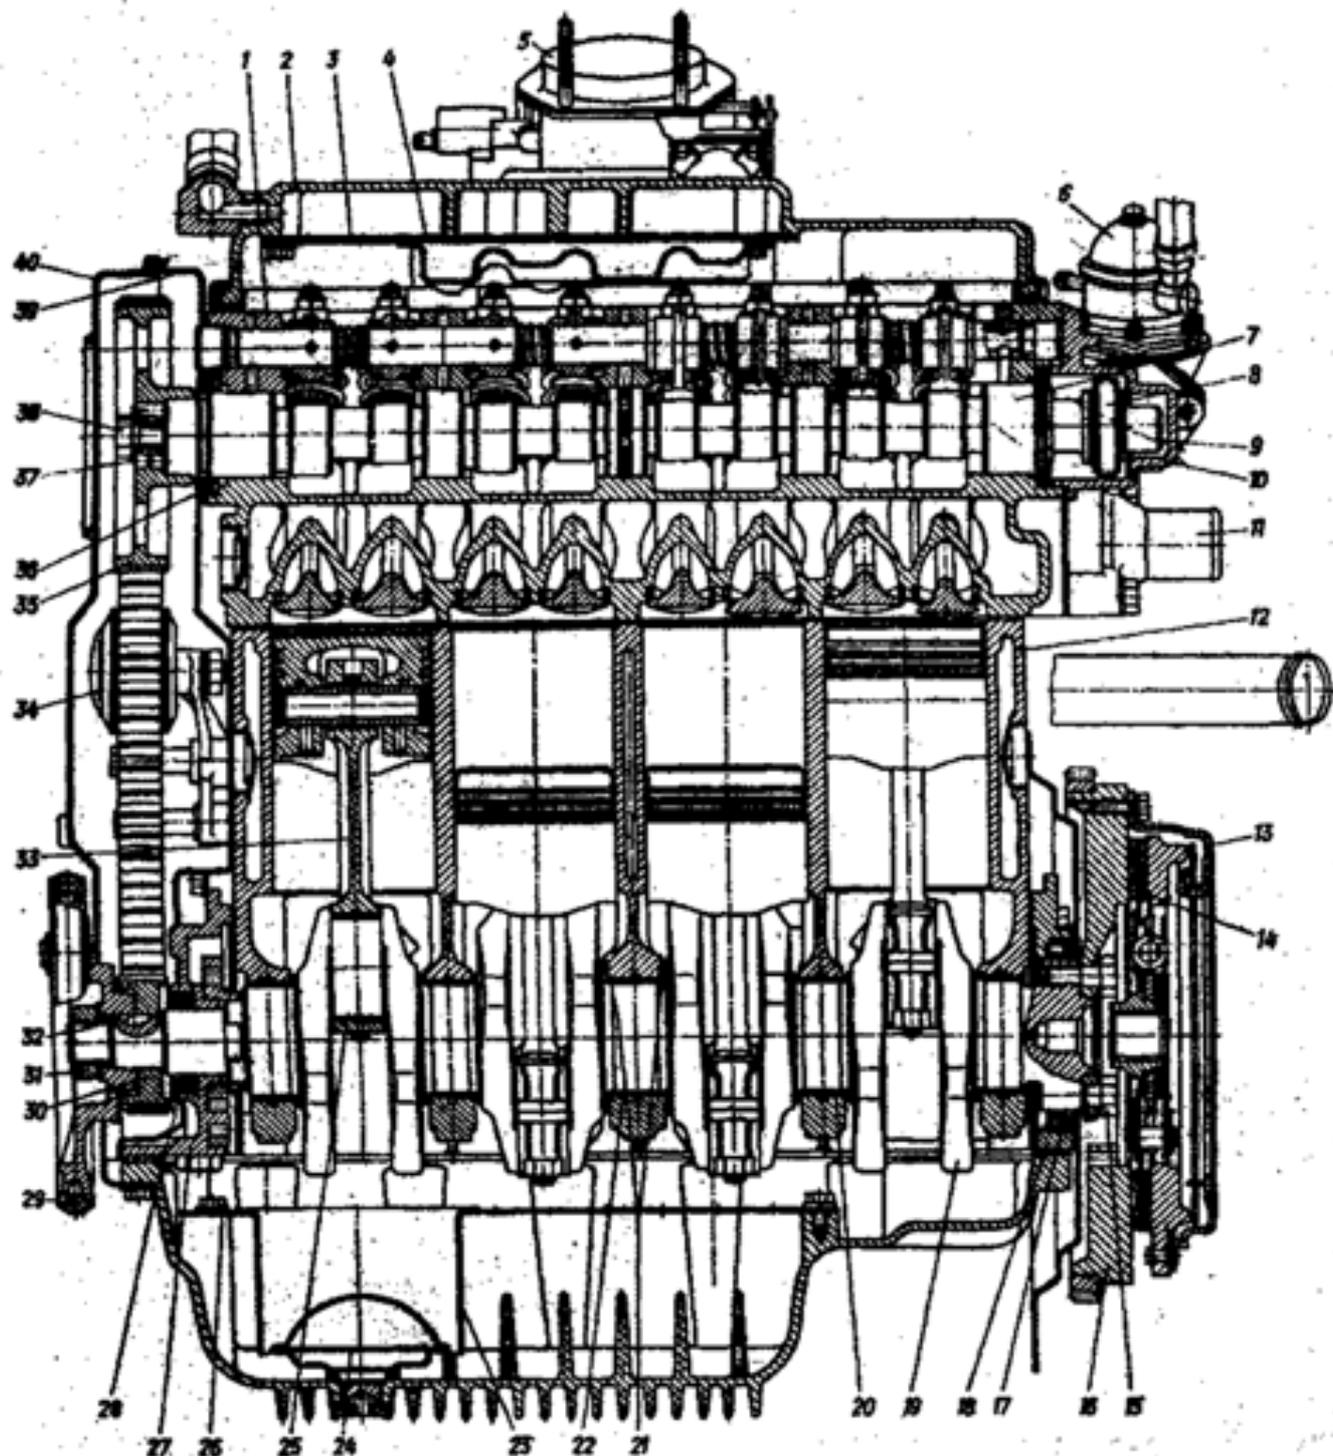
Продольный разрез двигателя: 1-головка цилиндров; 2-крышка головки цилиндров; 3, 4-прокладка и крышка маслоотделителя; 5-фланец карбюратора для крепления воздушного фильтра; 6-бензиновый насос; 7-вал распределительный; 8-ведущая шестерня привода датчика распределителя; 9-кулачок привода бензинового насоса; 10-корпус привода датчика-распределителя и бензинового насоса; 11-отводящий патрубок; 12-блок цилиндров; 13-нажимной диск сцепления; 14-диск сцепления ведомый; 15,38-болты; 16-маховик; 17,28,36-манжеты; 18-держатель манжеты; 19-коленчатый вал; 20-вкладыши коренных подшипников коленчатого вала; 21-упорные полукольца коренного подшипника коленчатого вала; 22-вкладыш среднего коренного подшипника коленчатого вала; 23-приемник масляного насоса; 24-маслосливная пробка; 25-вкладыш нижней головки шатуна; 26-масляный картер; 27-масляный насос; 29-шкив привода генератора; 30-ведущий шкив коленчатого вала; 31-гайка; 32-шпонка; 33-шатун с поршнем, поршневыми кольцами и пальцем; 34-натяжной ролик; 35-шкив привода распределительного вала; 37-стопорная шайба; 39,40-внутренний и наружный кожухи плоскос зубчатого ремня.
